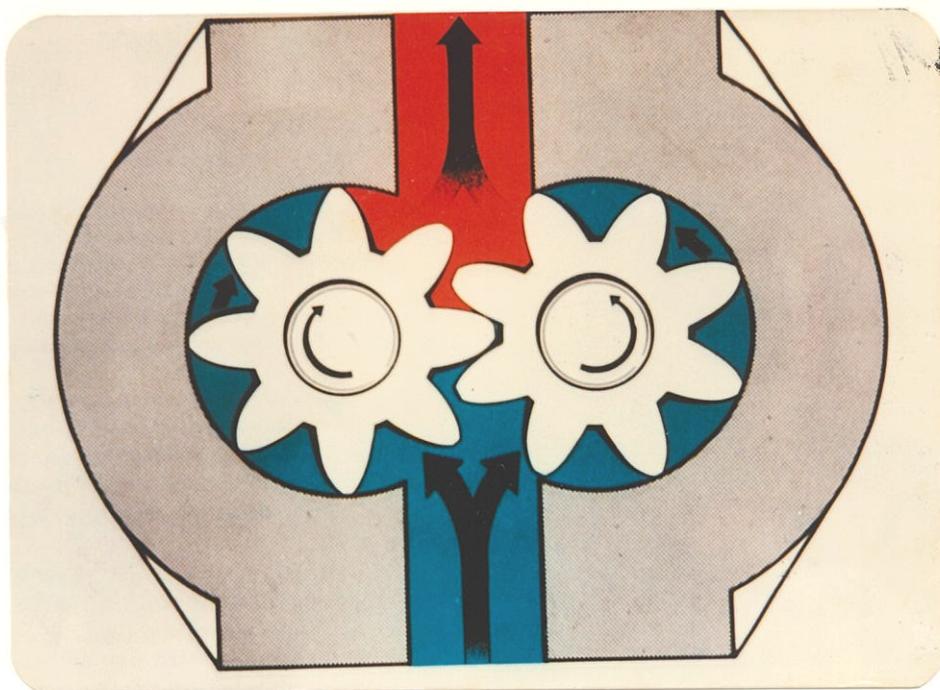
FUNCIONAMIENTO DE BOMBA HIDRAULICA DE ENGRANAJES.
